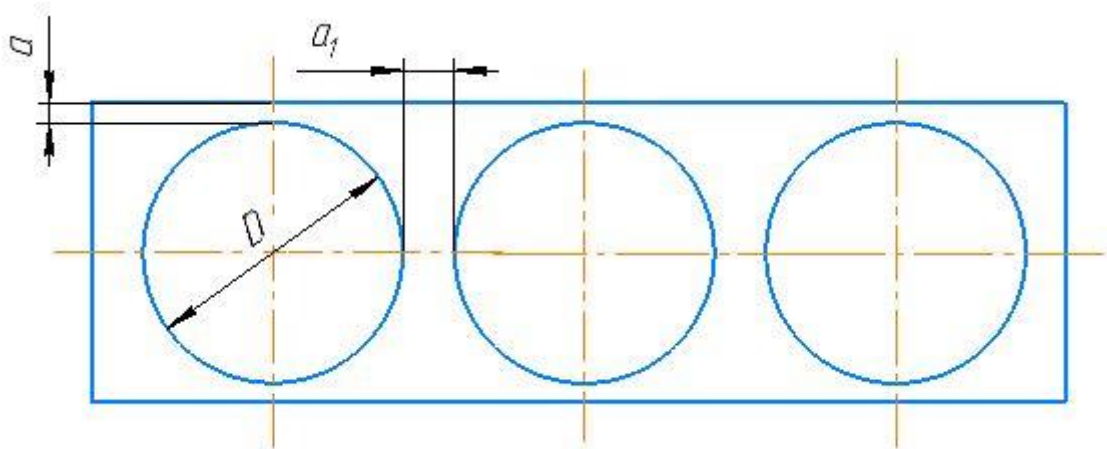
Схема раскроя листов на заготовки
